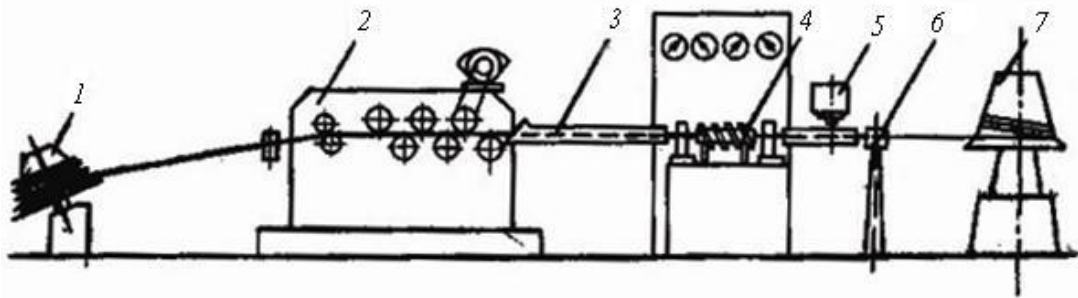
Схема установки волочіння з підгрівом СВЧ: 1-розмотувальний барабан; 2-вирівнювально-роликова машина; 3-трубка; 4-індуктор; 5-мельниця; 6-волока; 7-намотувальний барабан
